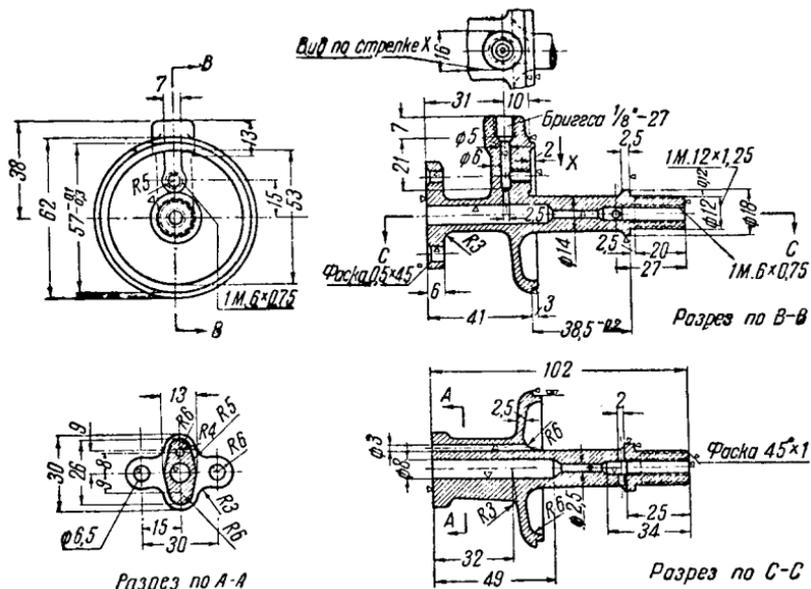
Дет. № 353. Крышка поплавковой камеры для воды
